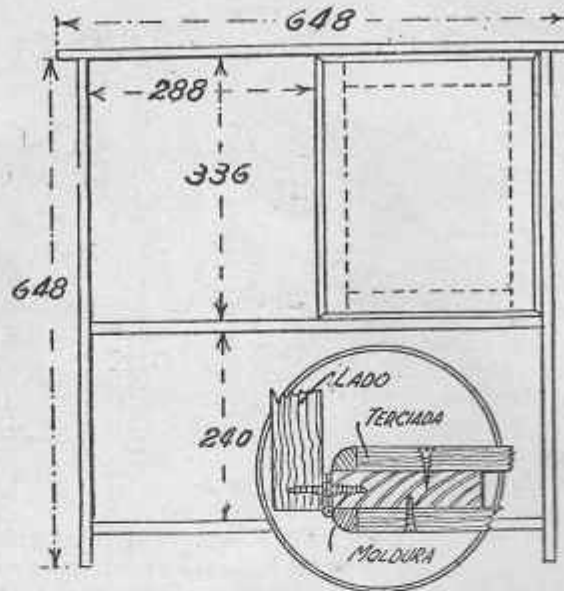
VISTA FRONTAL CON DIMENSIONES
